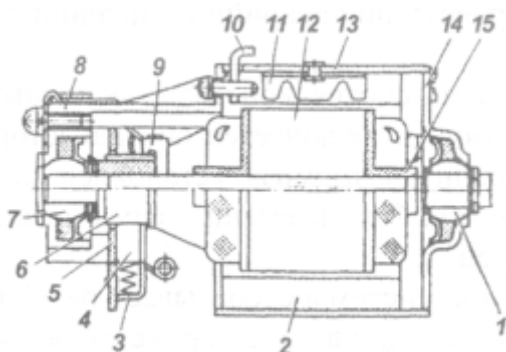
Электродвигатель с возбуждением от постоянных магнитов: 1,7 - подшипник; 2 - постоянный магнит; 3 - щеткодержатель; 4 - щетка; 5 - траверса; 6 - коллектор; 8, 14 - крышки; 9 - катушка индуктивности; 10 - крепежная пластина; 11 - пружина крепления магнита; 12 - якорь; 13 - корпус; 15 - изоляционная пластина якоря.
